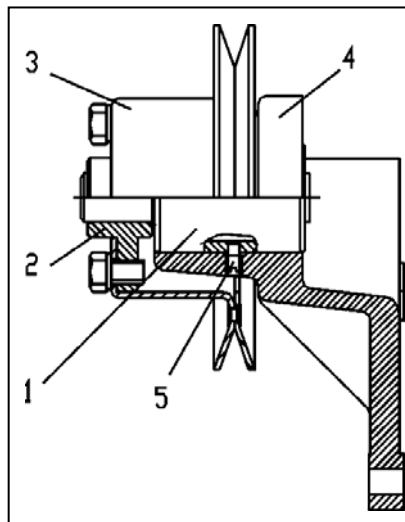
Корпус привода вентилятора в сборе для двигателя 4215.
